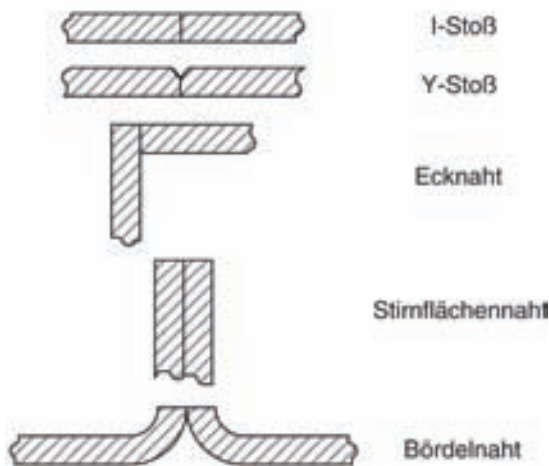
Typische Fugen für das Plasmaschweißen
